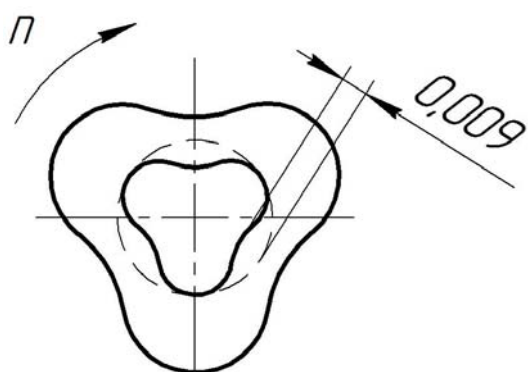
Деформации сварного корпуса зажатого в патроне в процессе нарезания резьбы
